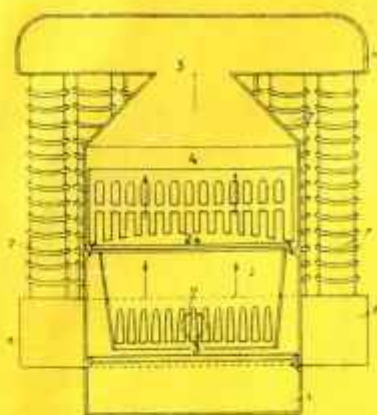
Fig. I. — Vue de face de l'ensemble du dispositif breveté.
